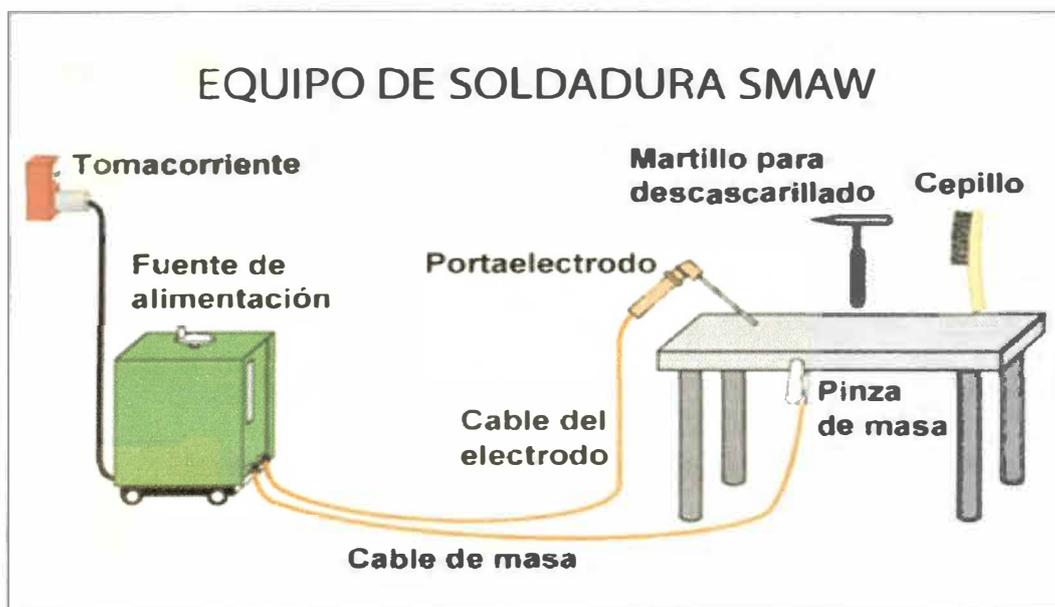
Soldadura SMAW. (Fuente: <http://www.demaquinasyherramientas.com/>)
